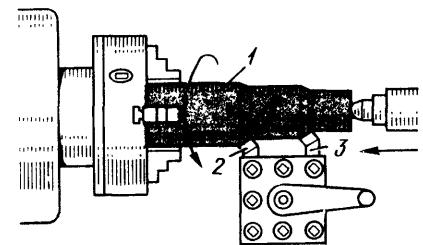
Закрепление заготовок в патроне с подвижным задним центром:
